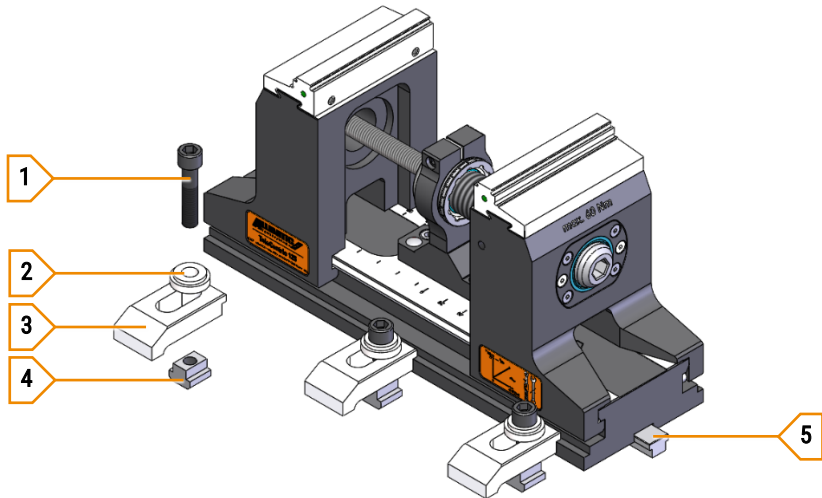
TeleCentric 125 – Befestigung mit Spannpratzen
